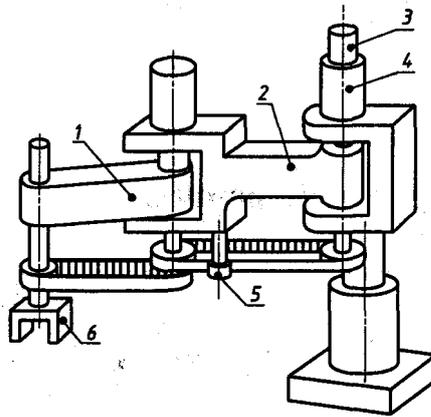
Механизм с зубчатыми ремнями движения кисти промышленного робота:
